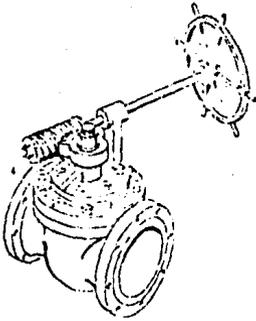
Válvula macho con actuador de engrane recto y - sin-fin.
